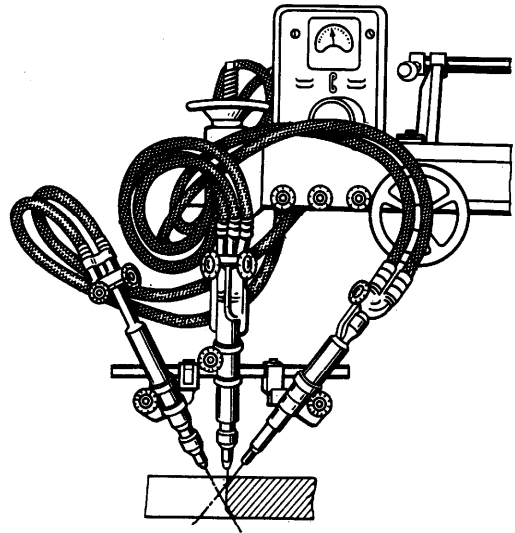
Одновременная резка и разделка кромок под сварку тремя резаками
